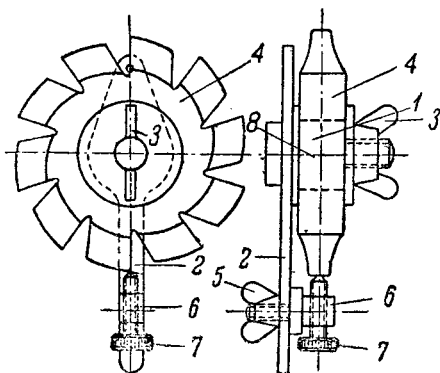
Шаблон для проверки высоты зубцов фрезы.
